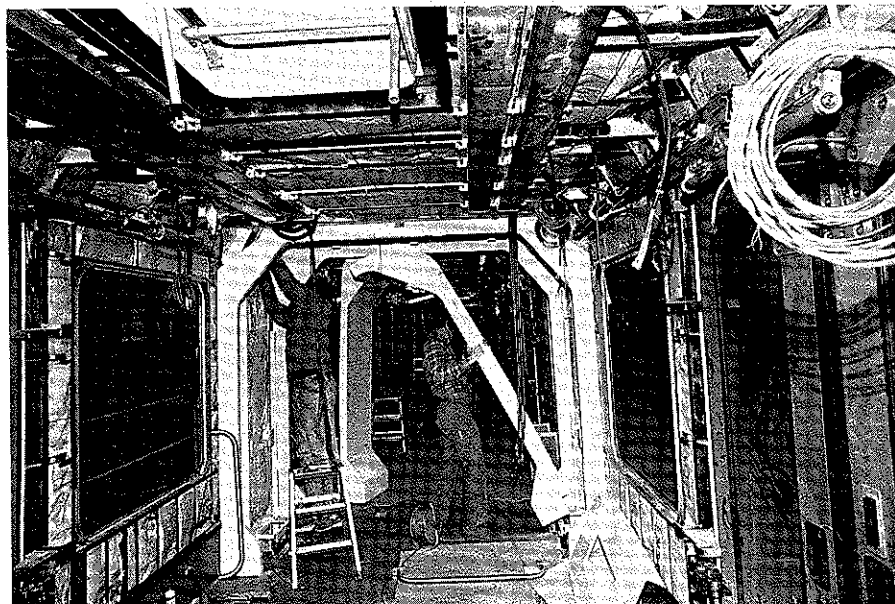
Travaux de montage à l'intérieur du caisson.
